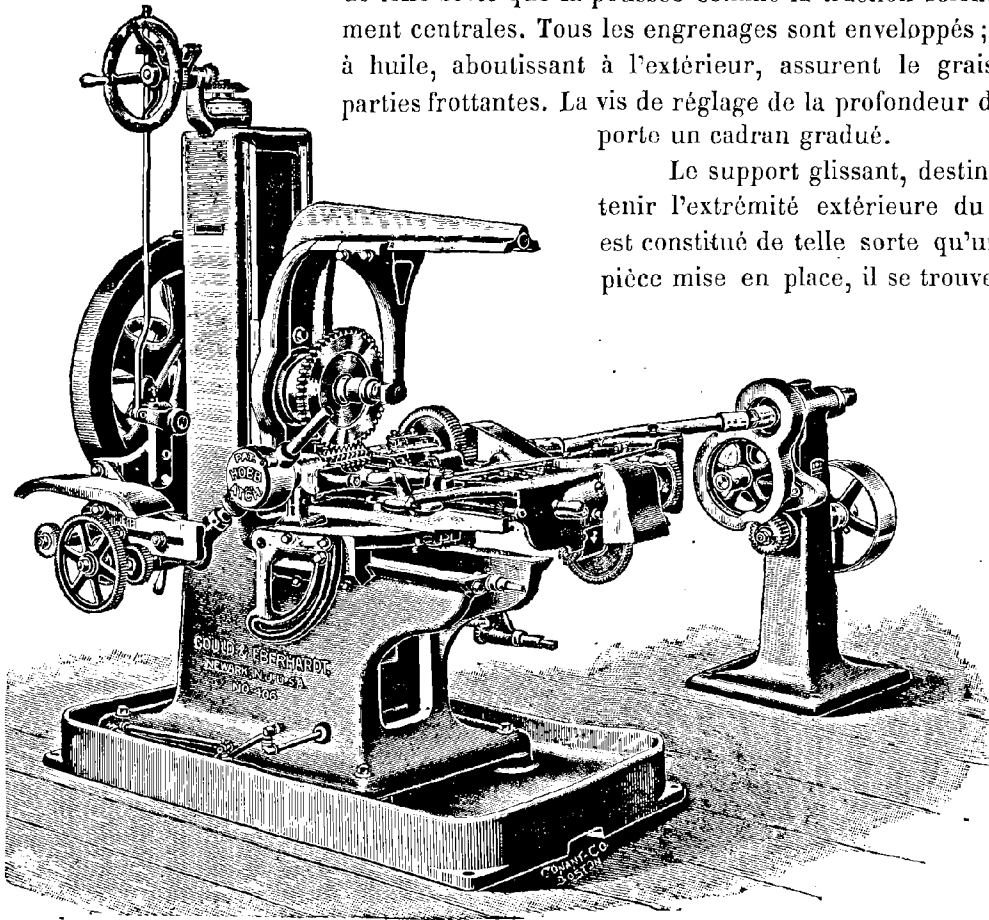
Machine de Gould et Eberhardt avec dispositif pour le taillage des roues à vis sans fin par vis-mère.
